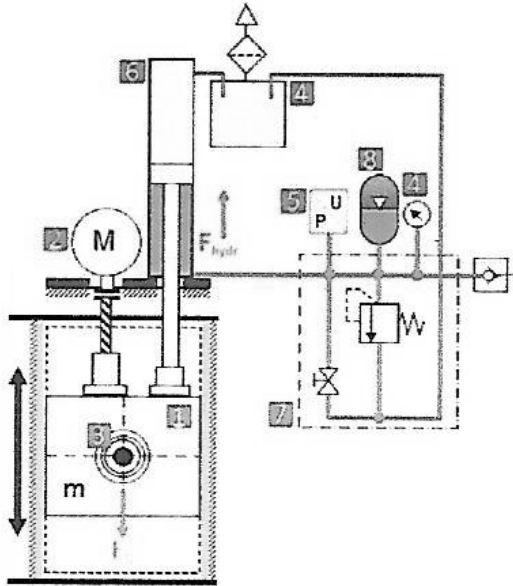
Prinzipschaltbild für hydraulischen Gewichtsausgleich
